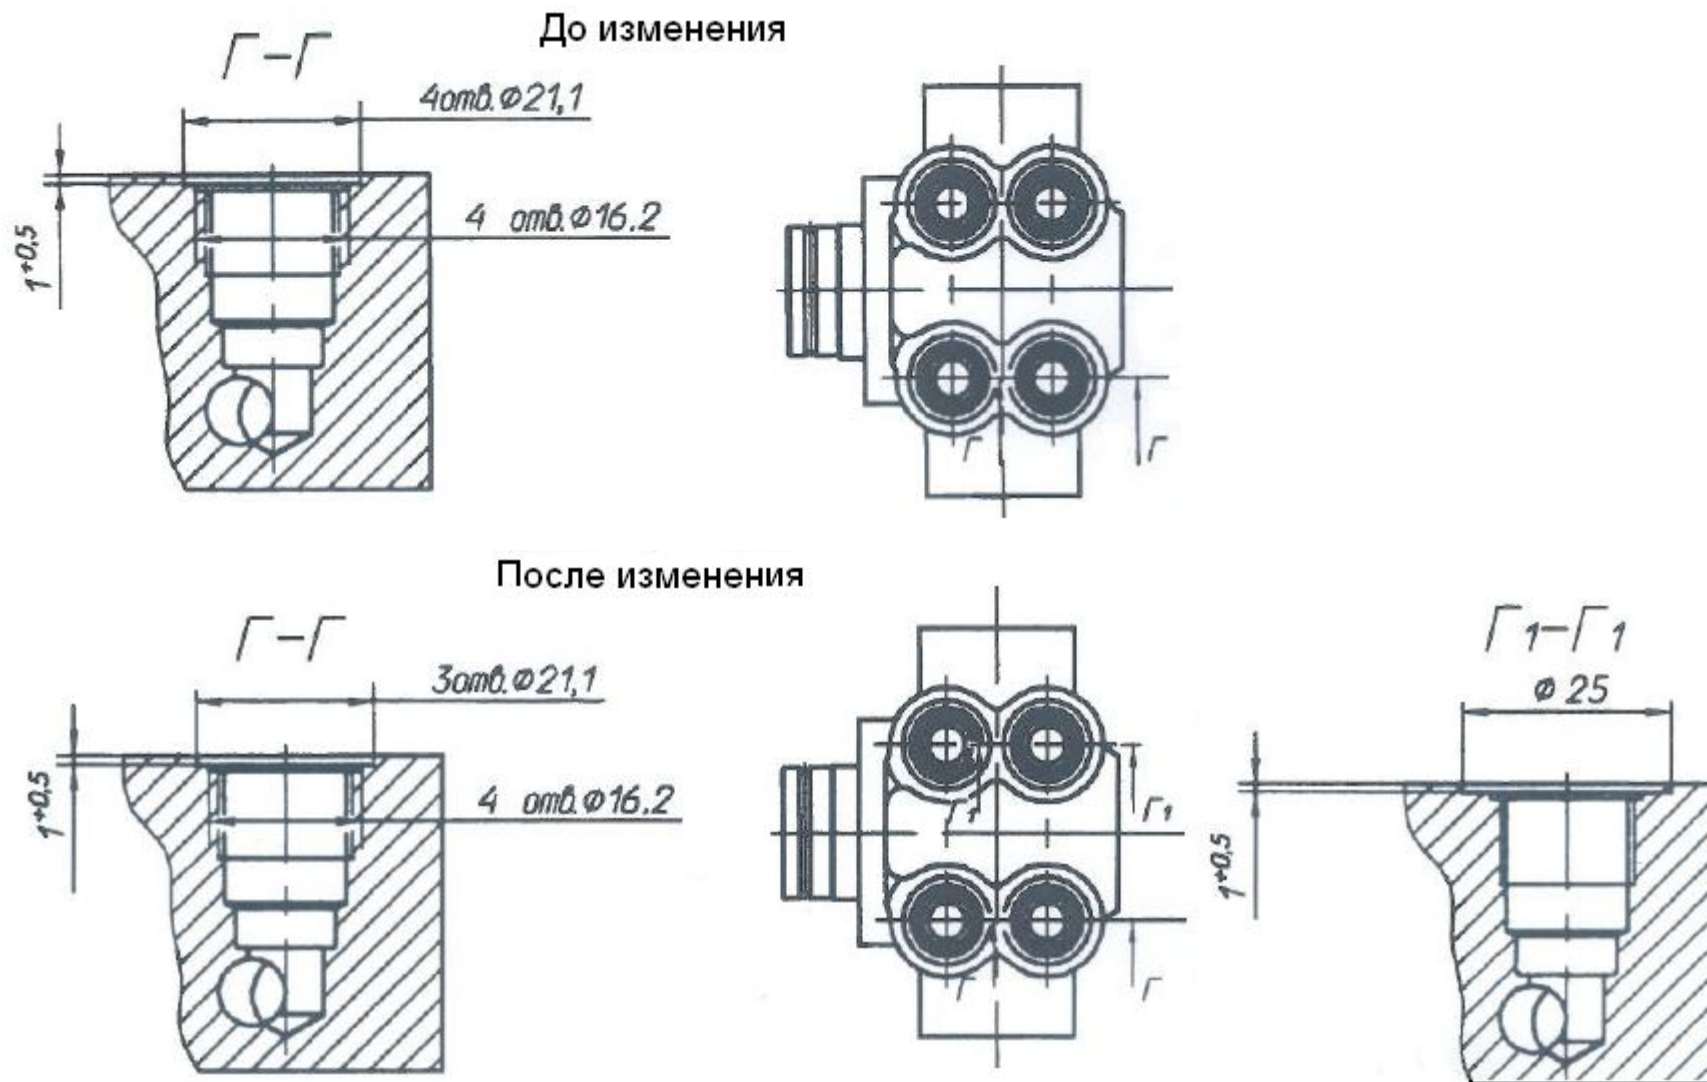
Корпус топливopодкачивающего насоса 44.1106016-01
